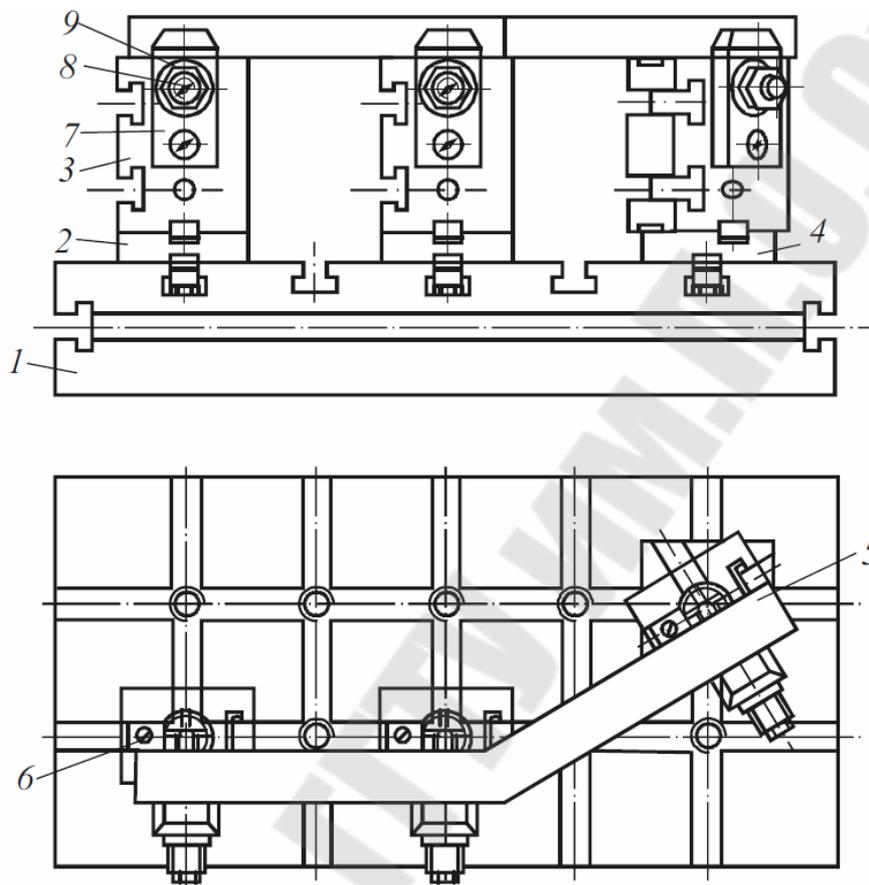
Универсально-сборное приспособление для фрезерования плоскости рычага [4]
